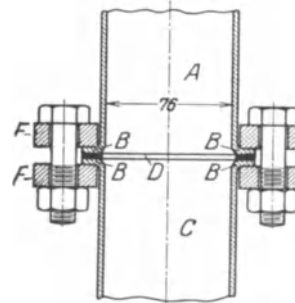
Aufgebördelte Bordringe mit Überwurfflanschen.
